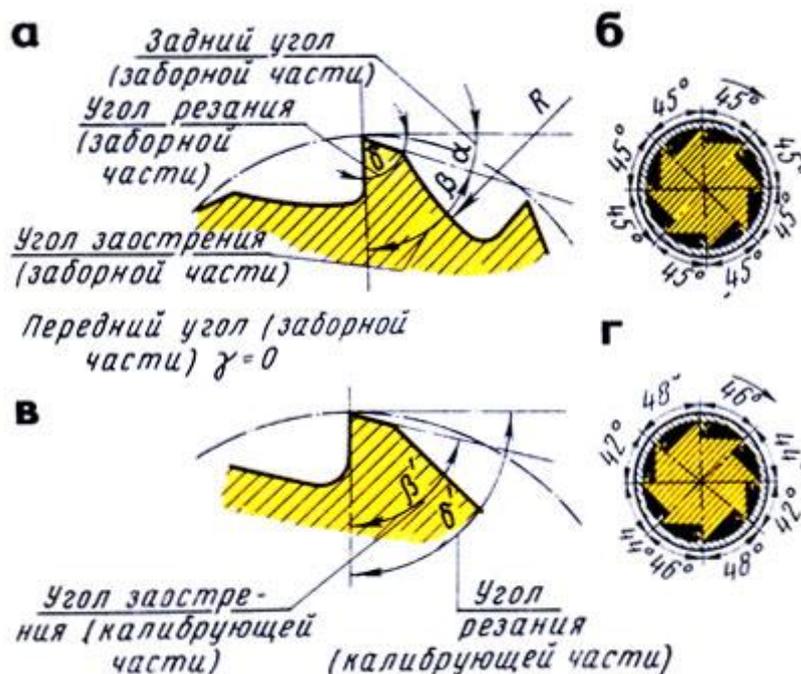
Геометрия зубьев развертки: а, в - элементы геометрии, б - развертка с равномерным шагом, г - с неравномерным шагом
